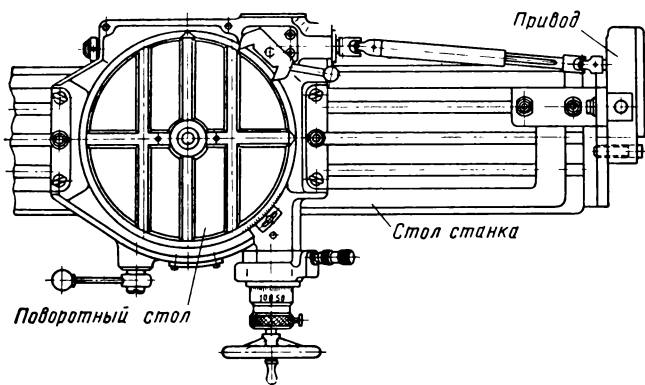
Схема присоединения механического привода от фрезерного станка к поворотному круглому столу
